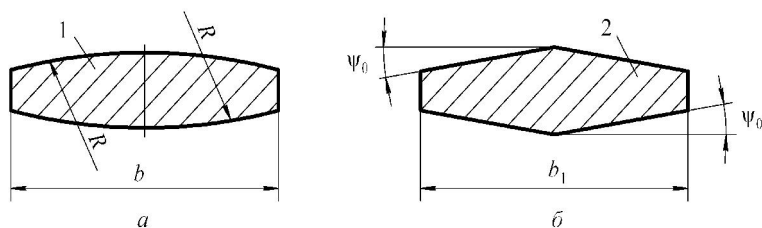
Сечения наружного и бочкообразного зуба 1 втулки (а) и внутреннего скошенного зуба 2 обоймы (б)
